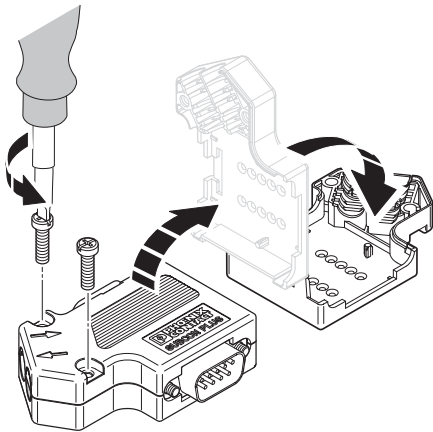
Montage des D-SUB-Steckers für rechtsseitige Kabelzuführung
